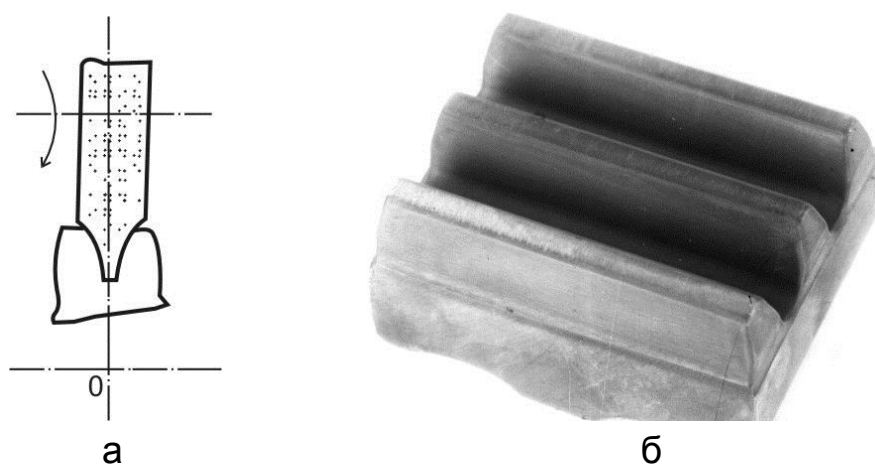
Схема шлифования зубчатого колеса на станке 5861 (а), внешний вид прижога (б)
